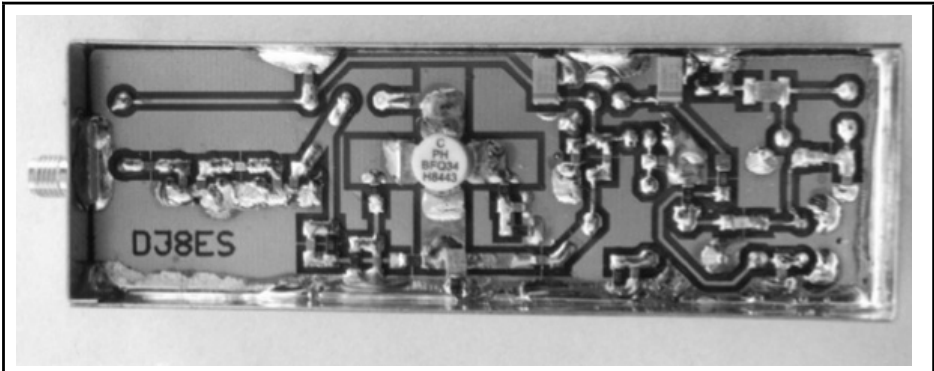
145MHz oscilátor pripravený na prevádzku, zobrazenie SMD komponentov na fóliovej strane PCB.
